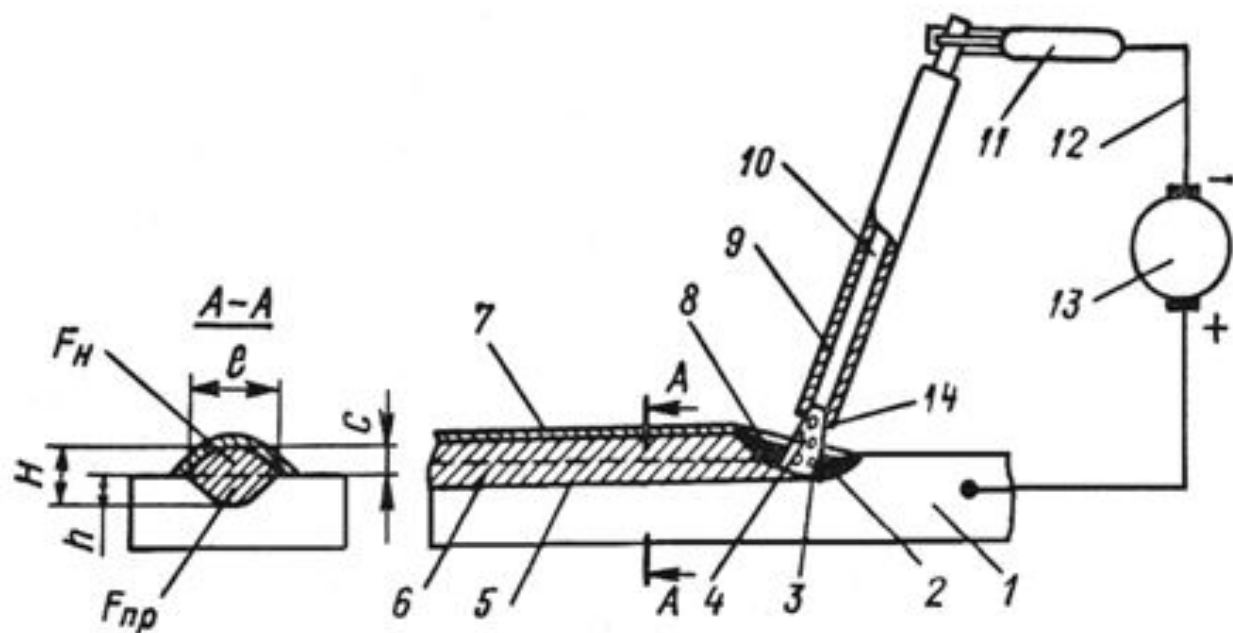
Схема ручной сварки покрытым электродом: 1 — основной металл; 2 — сварочная ванна; 3 — кратер; 4 — сварочная дуга; 5 — проплавленный металл; 6 — наплавленный металл; 7 — шлаковая корка; 8 — жидкий шлак; 9 — покрытие электрода; 10 — стержень электрода; 11 — электродержатель; 12 — сварочная цепь; 13 — источник питания; 14 — козырек. ¶
